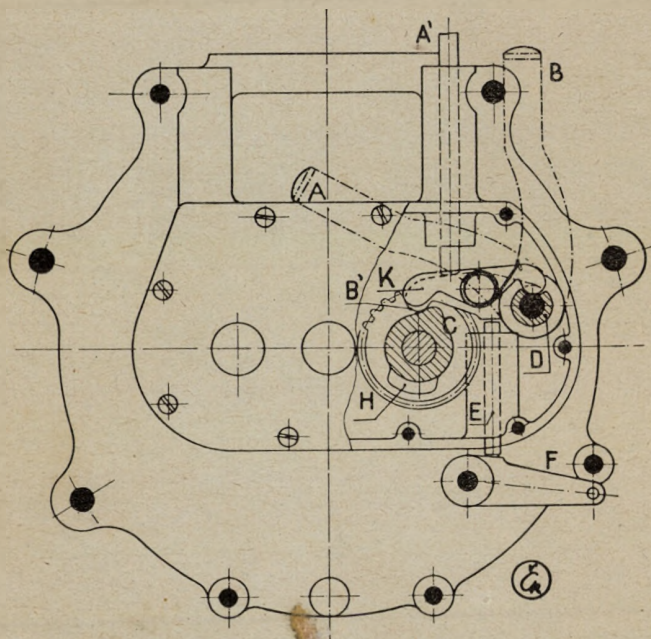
Samočinný dekompresor soustavy „P. & M.“
